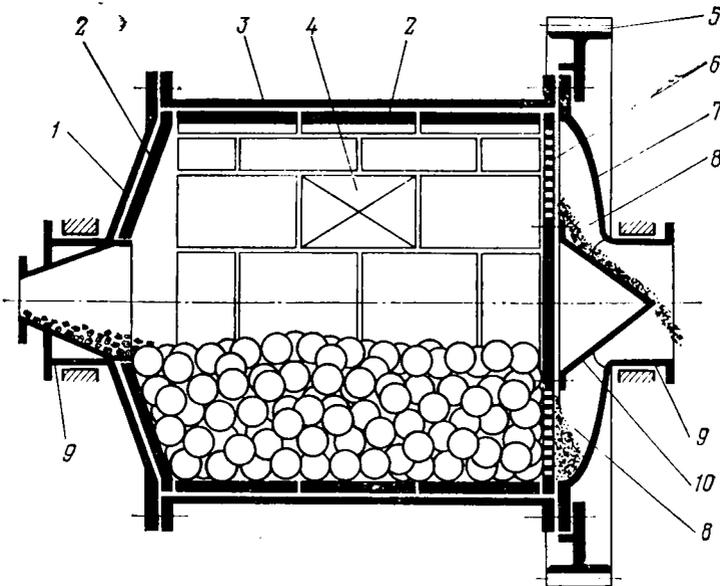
Схема шарового диафрагменного измельчителя:
